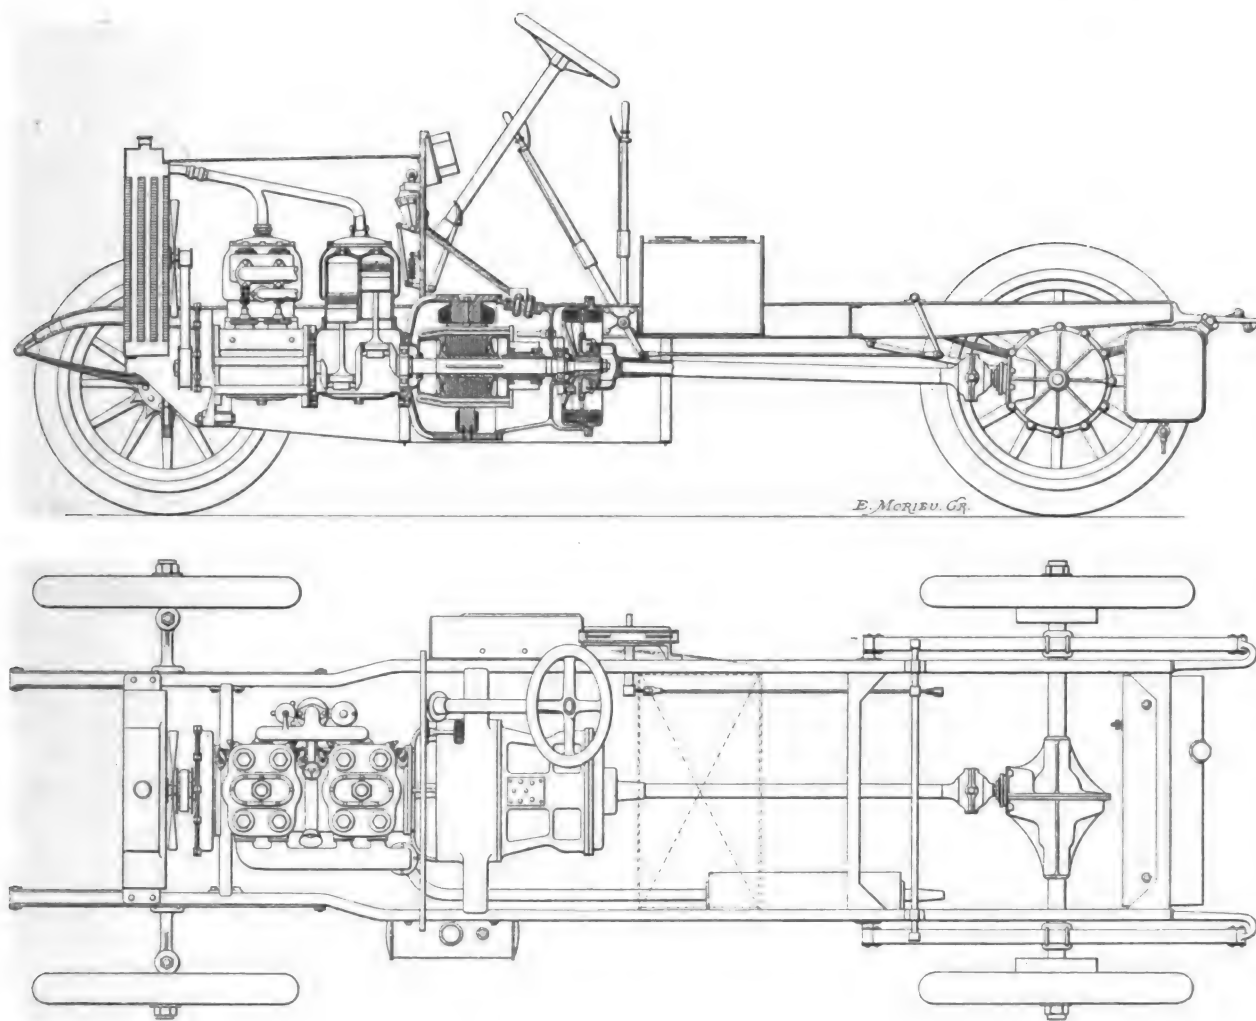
Coupe longitudinale, élévation et plan du châssis.
